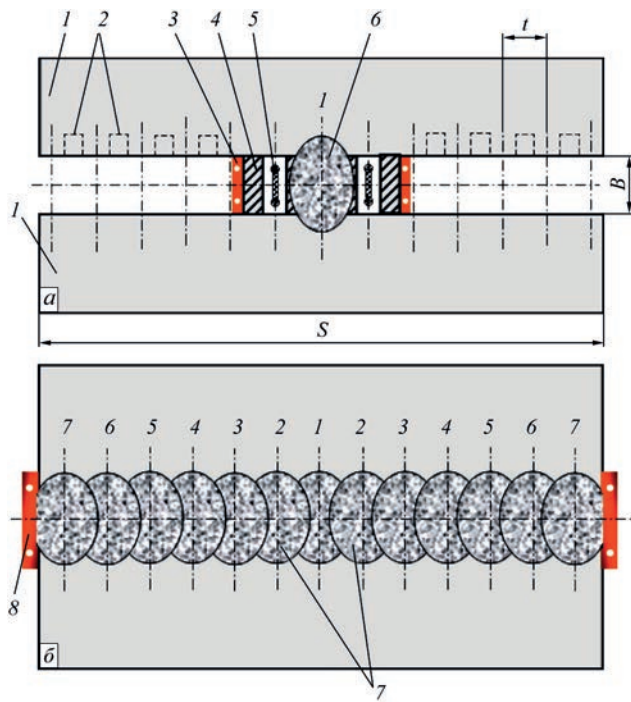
Схема розмітки стику, зварки центральної комірки (а) і виконання суміжних проходів БЕШЗ ПМ (б): 1 – зварювані частини дефектної деталі; 2 – місця установки формуючих вставок; 3, 8 – водоохолоджувальний пристрій; 4 – вставка; 5 – плавкий мундштук; 6 – центральний шов; 7 – суміжні шви;  $S$  – товщина деталі (довжина наскрізної тріщини);  $B$  – проміжок;  $t$  – крок комірок
